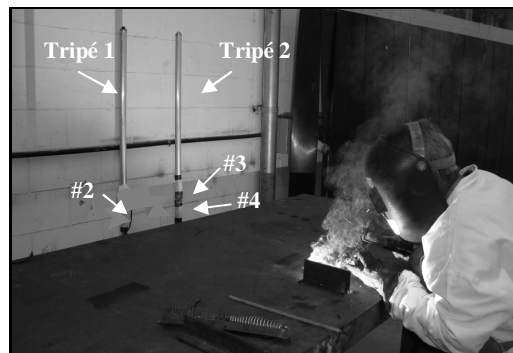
Posição dos conjuntos (cartão+lâmina+filtro), nos tripés, expostos à RUV durante 2 min de soldagem elétrica.
